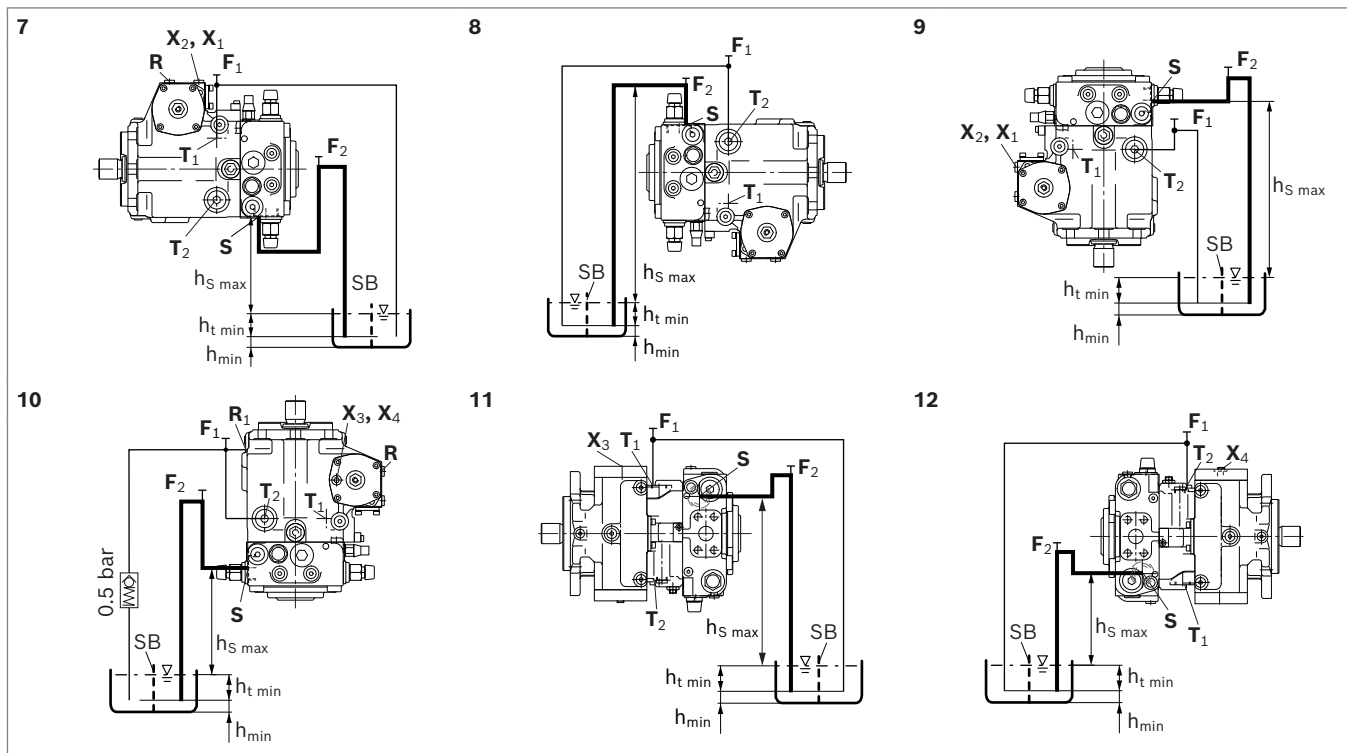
Установка над баком A4VG с монтажным положением 7-12
